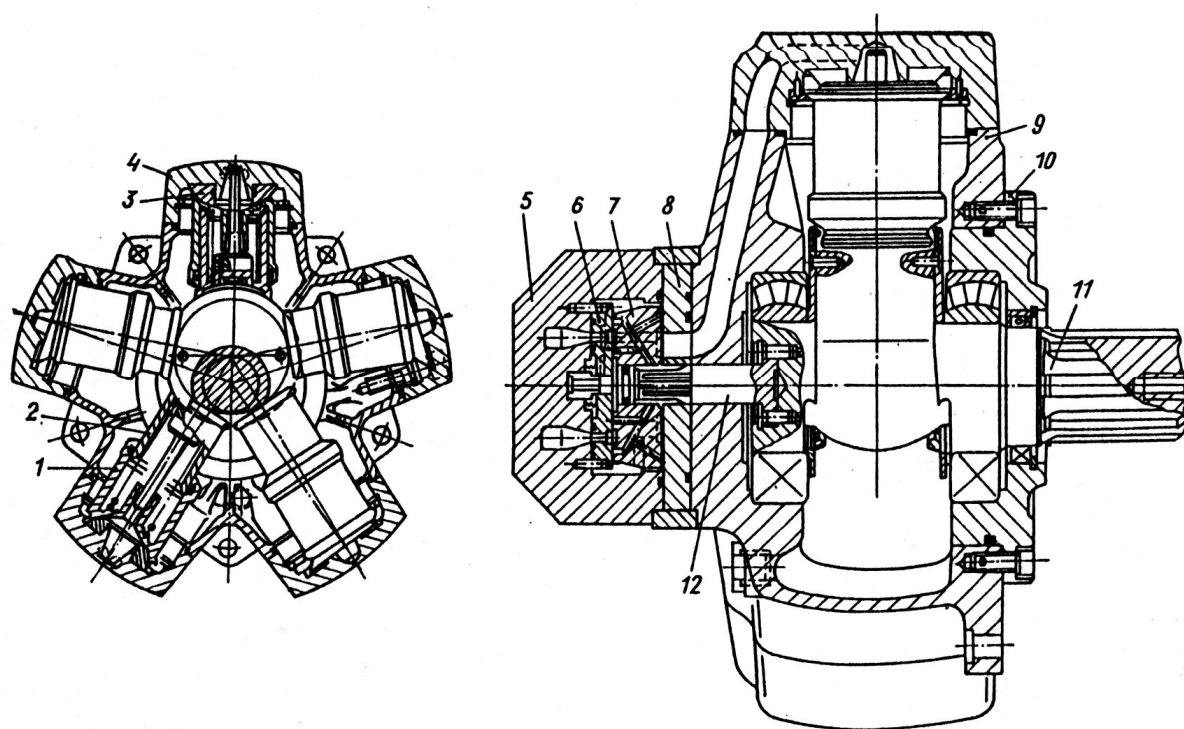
Радиально-поршневой гидромотор типа МР:
